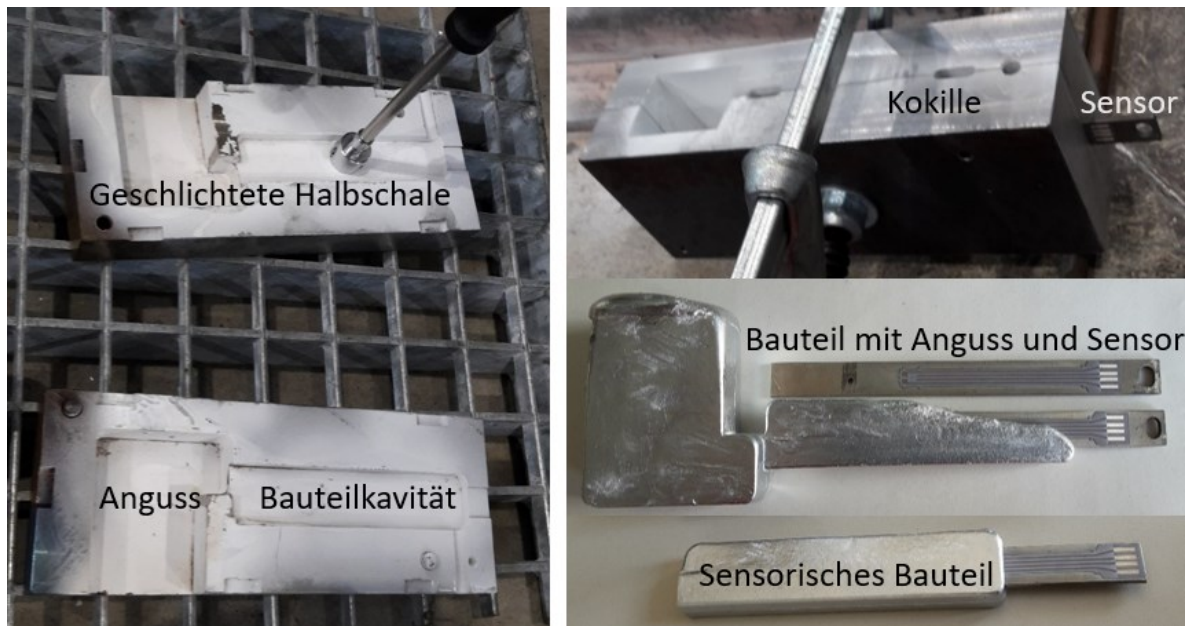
Übersicht zum Versuchsumfeld im Kokillenguss, Kokille aus geschichteten Halbschalen, der geschlossenen Kokille inklusive eingelegtem Sensor, dem Bauteil mit Anguss einer frühzeitig erstarrten Legierung; sowie einem sensorischen Bauteil.
